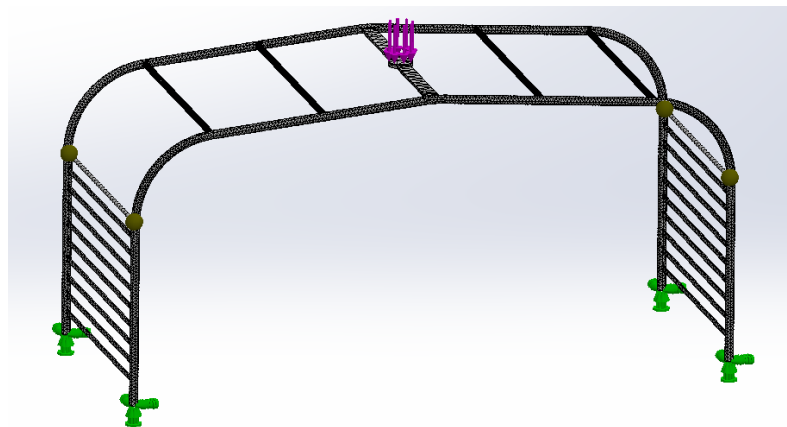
Vista del mallado de la estructura. Fuente: Propia.
